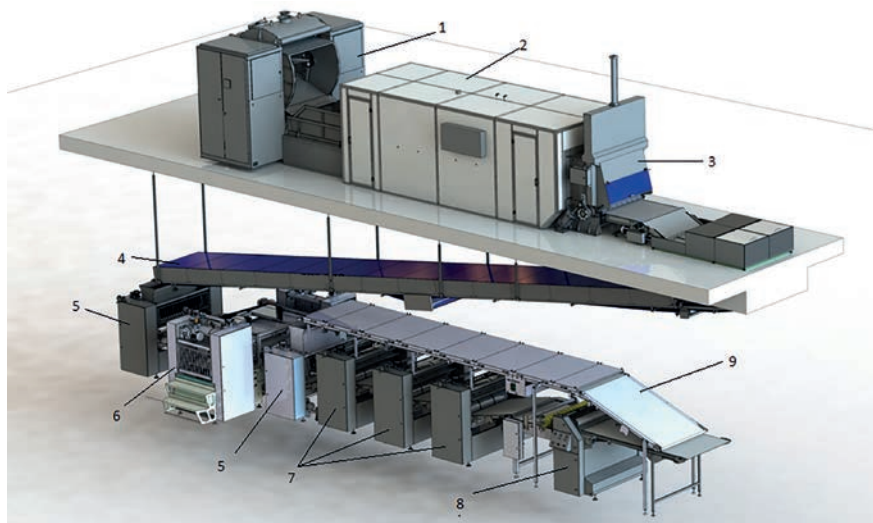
Загальний вигляд обладнання нової потокової лінії виробництва зтяжного печива КФ «Ярич»: 1 — тістомісильна машина; 2 — ферментаційна камера; 3 — гільйотина; 4 — конвеєр; 5 — тривалкова машина для отримання тістової стрічки з обрізків; 6 — ламінаторна установка з розкладником тістової стрічки; 7 — калібрувальні машини; 8 — роторна формувальна машина; 9 — транспортер обрізків.
